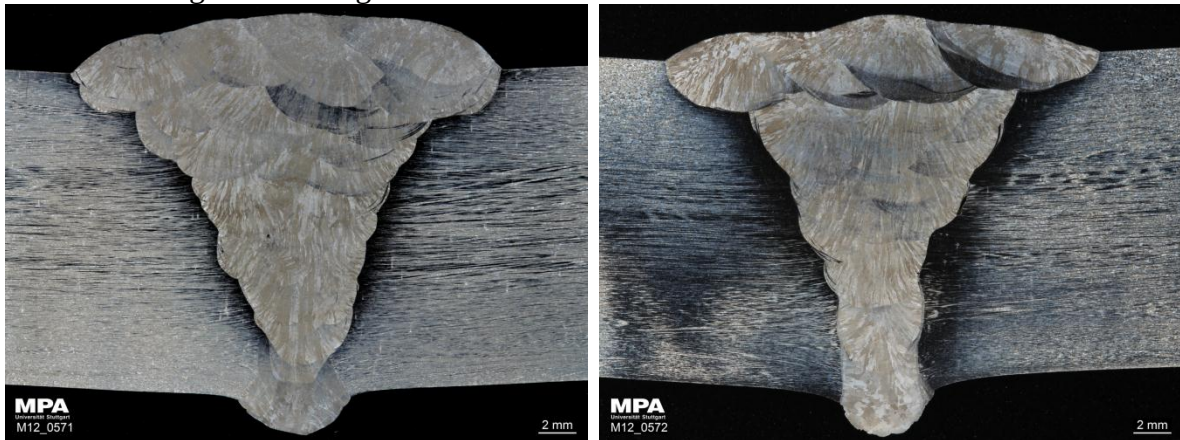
Schweißnähte unter Beeinflussung eines Elektromagnet geschweißt:
